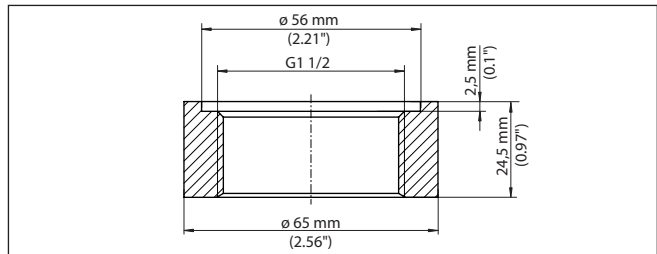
Maße Einschweißstutzen Gewinde G1½ (DIN 3852-A)
